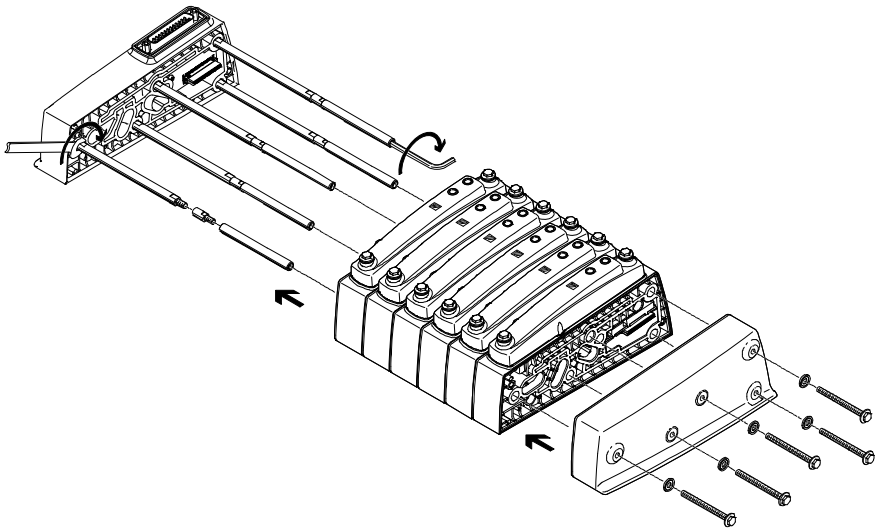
Verschraubung der Verkettungsplatten mittels Zuganker
